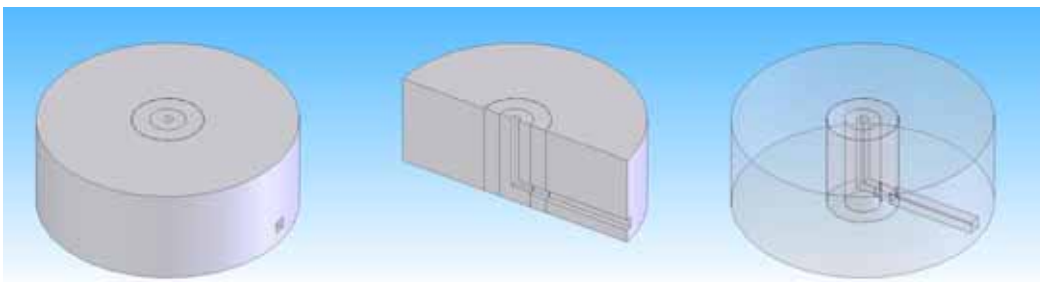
Trn upnutý v držáku (držák zprůhledněn)
